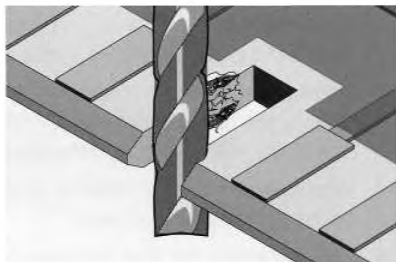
а – Удаление поврежденного участка твердосплавной торцевой фрезой
